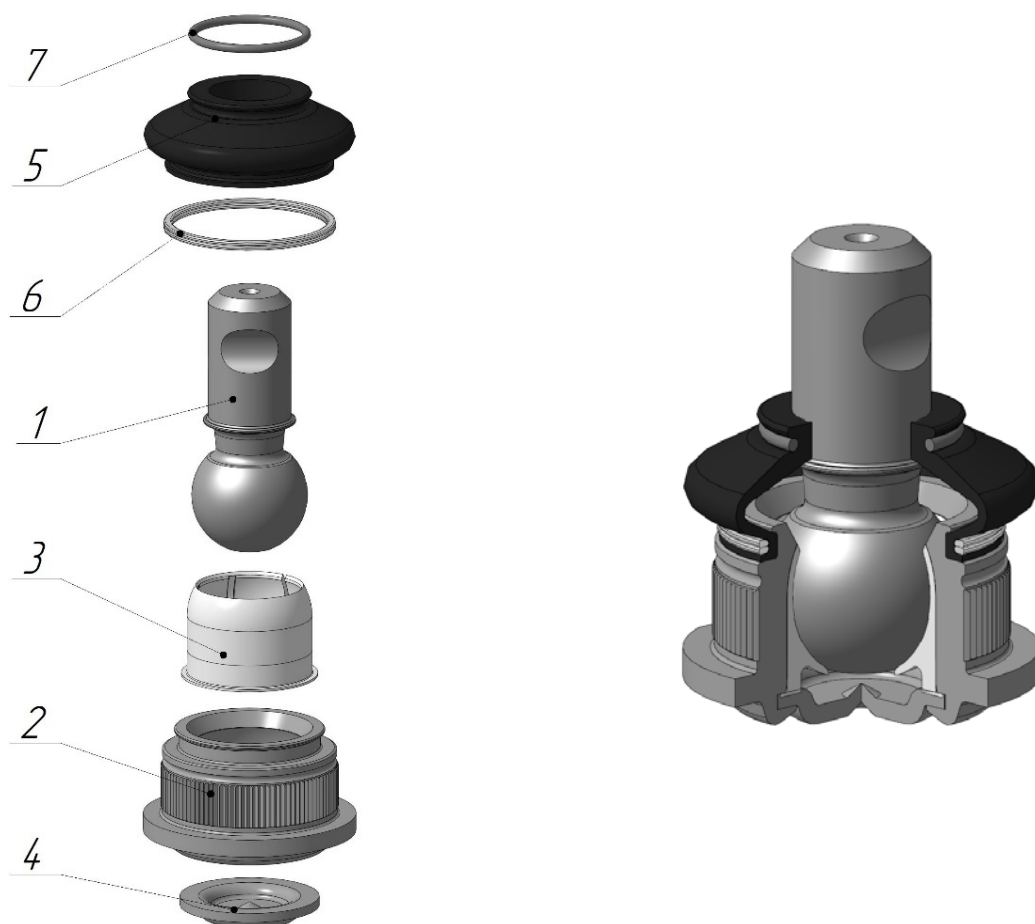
Конструкция шарового шарнира передней подвески автомобиля LADA Largus: 1 – шаровой палец; 2 – корпус; 3 – вкладыш; 4 – обойма; 5 – чехол защитный; 6 – кольцо пружинное; 7 – кольцо уплотнительное
